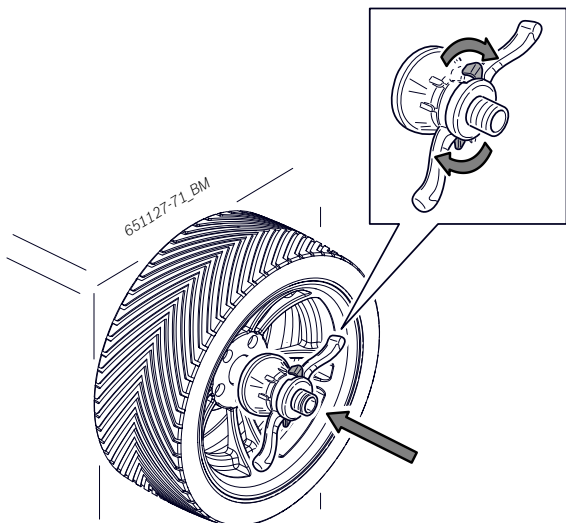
Glisser l'écrou à serrage rapide déverrouillé sur l'arbre
